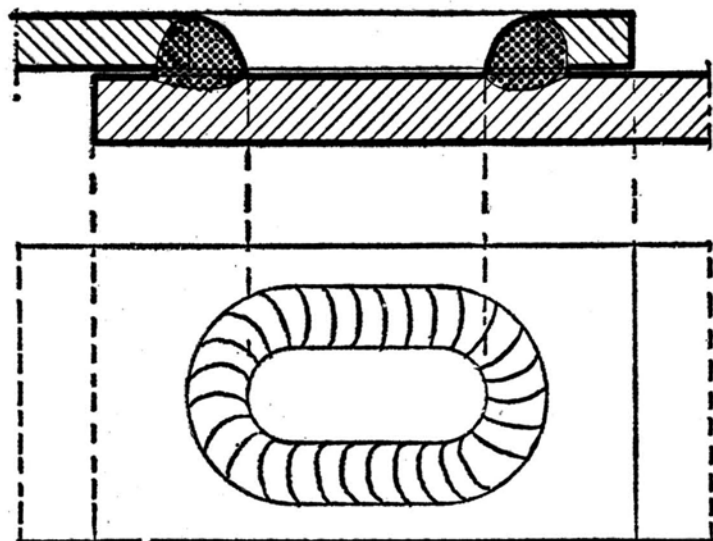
SOLDADURA DE ANGULO, EN RANURA
